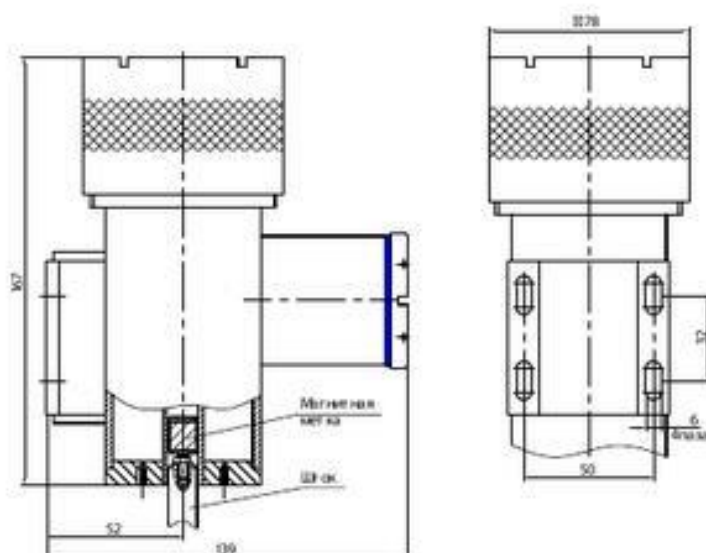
Габаритные и присоединительные размеры ПП МГДУ ЛП на лапках.
